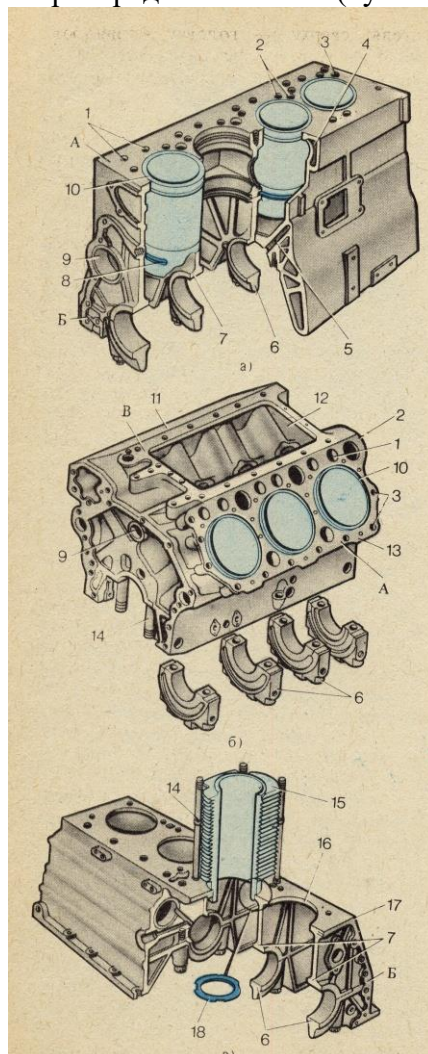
Блок - картеры двигателей: а - жидкостного охлаждения с рядным расположением цилиндров, б - жидкостного охлаждения с V - образным расположением цилиндров, в - воздушного охлаждения с рядным расположением цилиндров, 1 - отверстия для штанг толкателей, 2 - отверстия для отвода воды, 3 - отверстия для шпилек крепления головки цилиндров, 4 - водораспределительный канал, 5 - канал для подвода масла, 6 - крышка коренного подшипника, 7 - прилив, 8 - резиновое уплотнительное кольцо, 9 - отверстие для втулки распределительного вала, 10 - гильза цилиндра, 11, 13 - левый и правый полублоки, 12 - воздушная полость, 14 - шпилька, 15 - гильза цилиндра воздушного охлаждения, 16 - отверстие для гильзы цилиндра, 17 - картер, 18 - уплотнительная прокладка, А - плоскость крепления головки цилиндров, Б - плоскость крепления картера распределительных шестерен, В - плоскость крепления крышки с опорой под турбокомпрессор.
